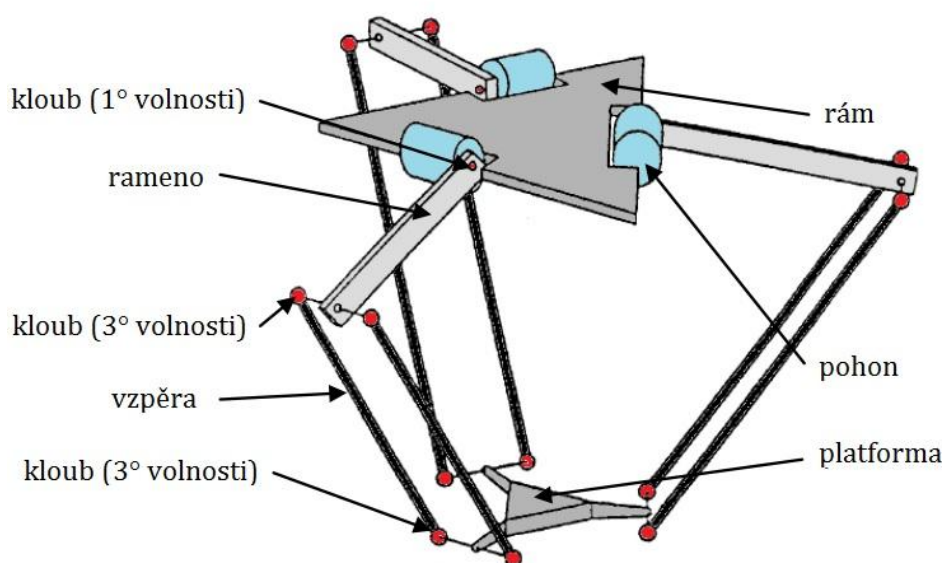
Manipulátor IRB FlexPicker od firmy ABB – převzato z [www.abb.com](http://www.abb.com)
